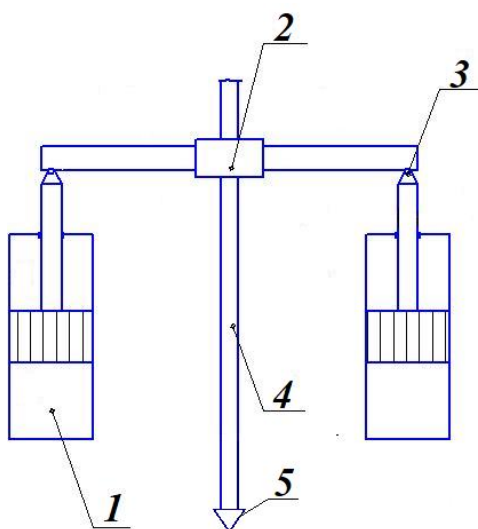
Схема поршневого типа подачи: 1 – гидро- или пневмоцилиндр; 2 – патрон; 3 – буровая штанга; 4 – буровой став; 5 – исполнительный орган
